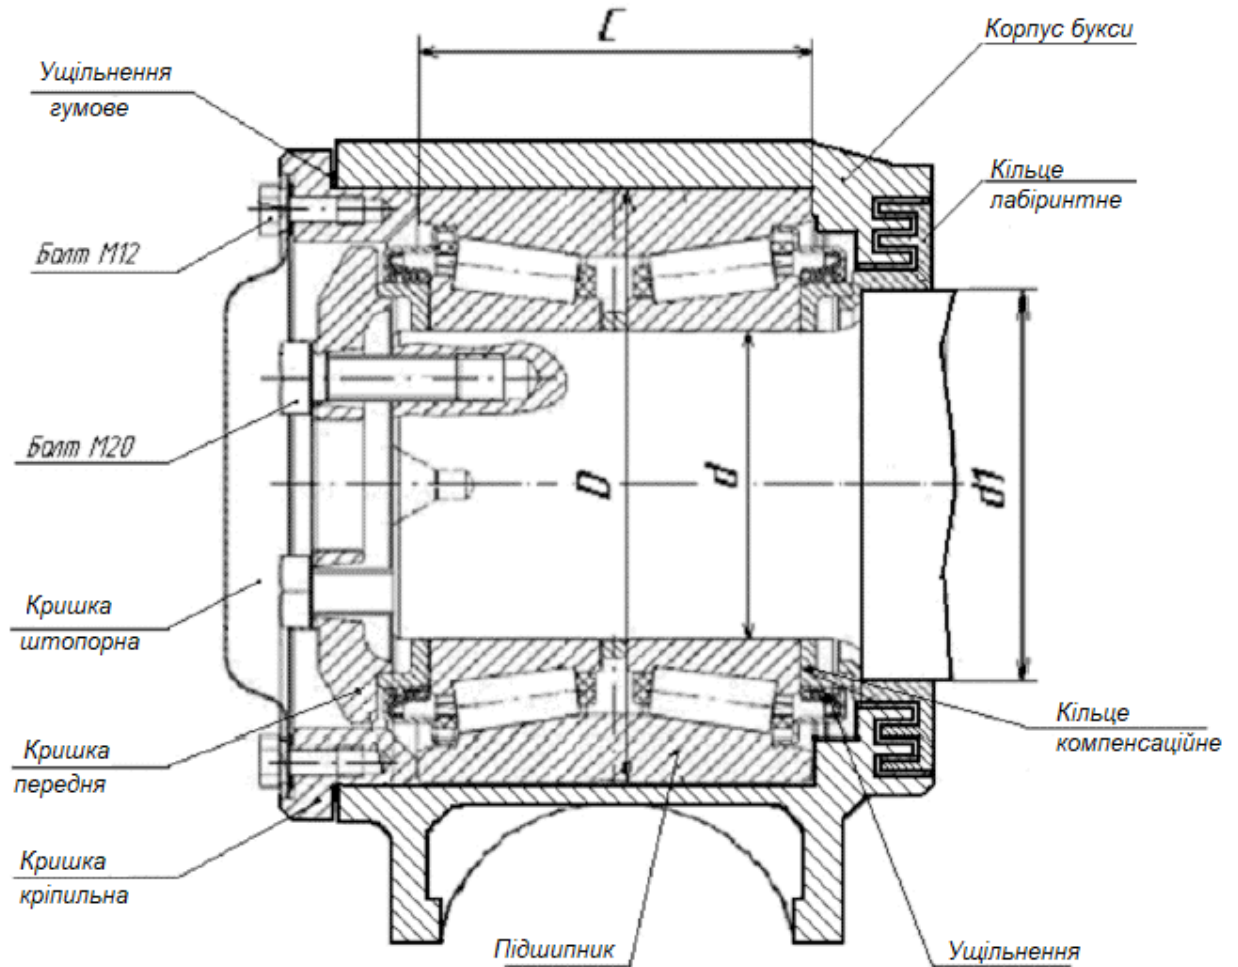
Підшипник касетного типу в габаритних розмірах
